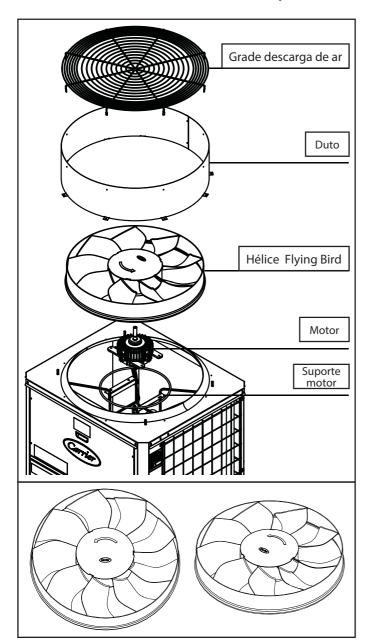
Vista explodida conjunto ventilador condensadora e Hélice Flying Bird
